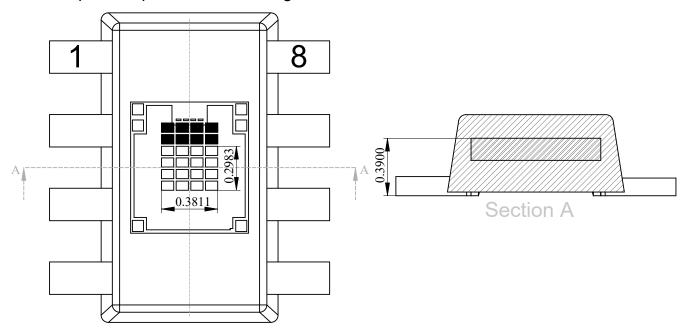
Package Orientation Visual Reference of Pin 1 (Top View) & Sectional View
